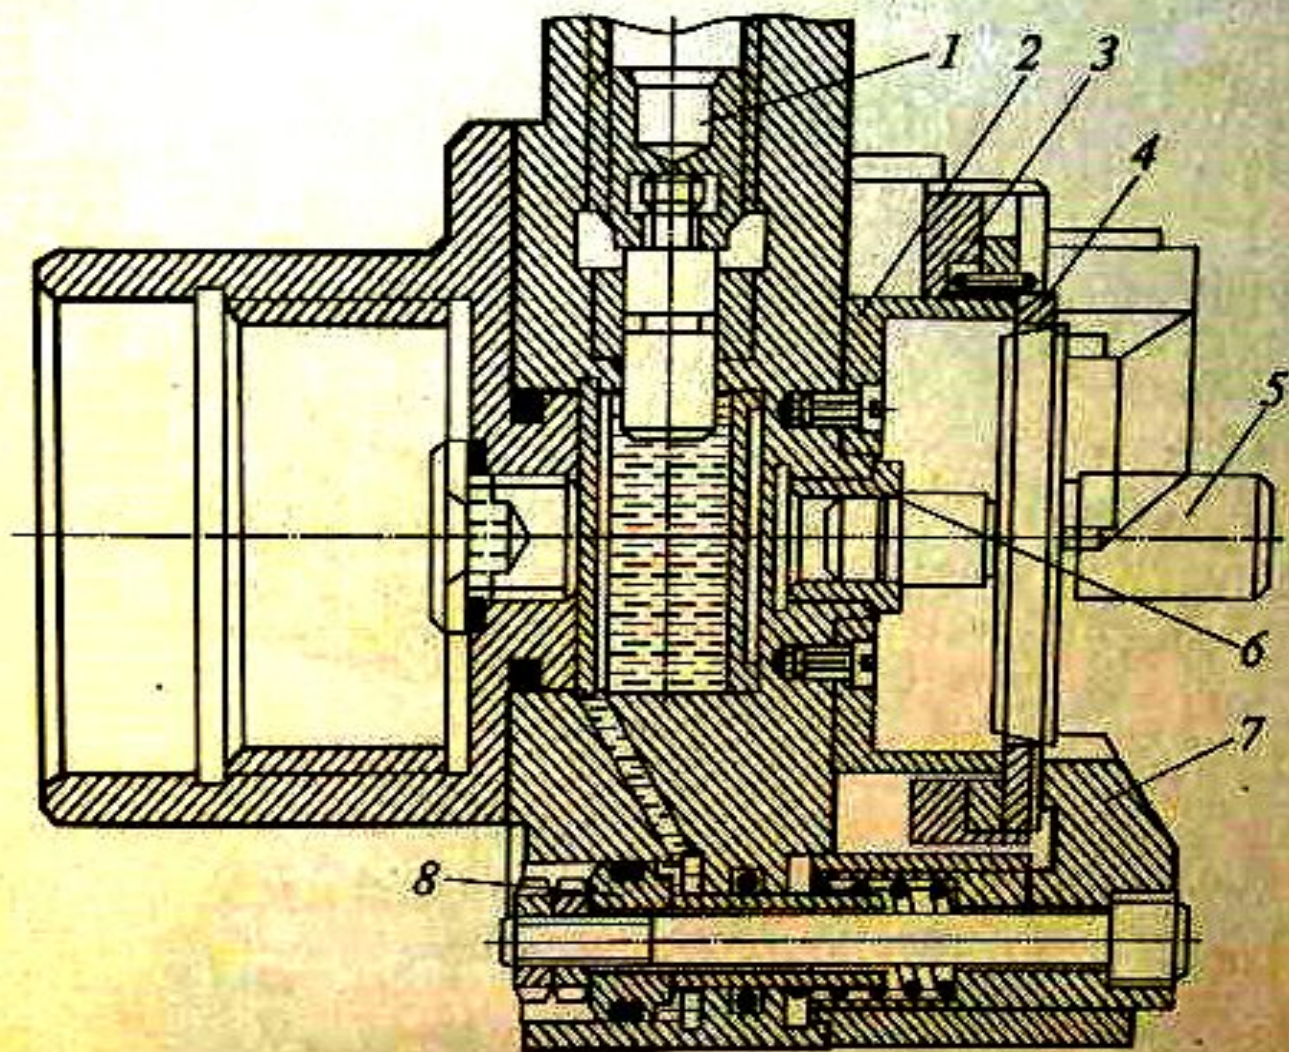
Специализированное приспособление для токарной обработки сегментных колец:
